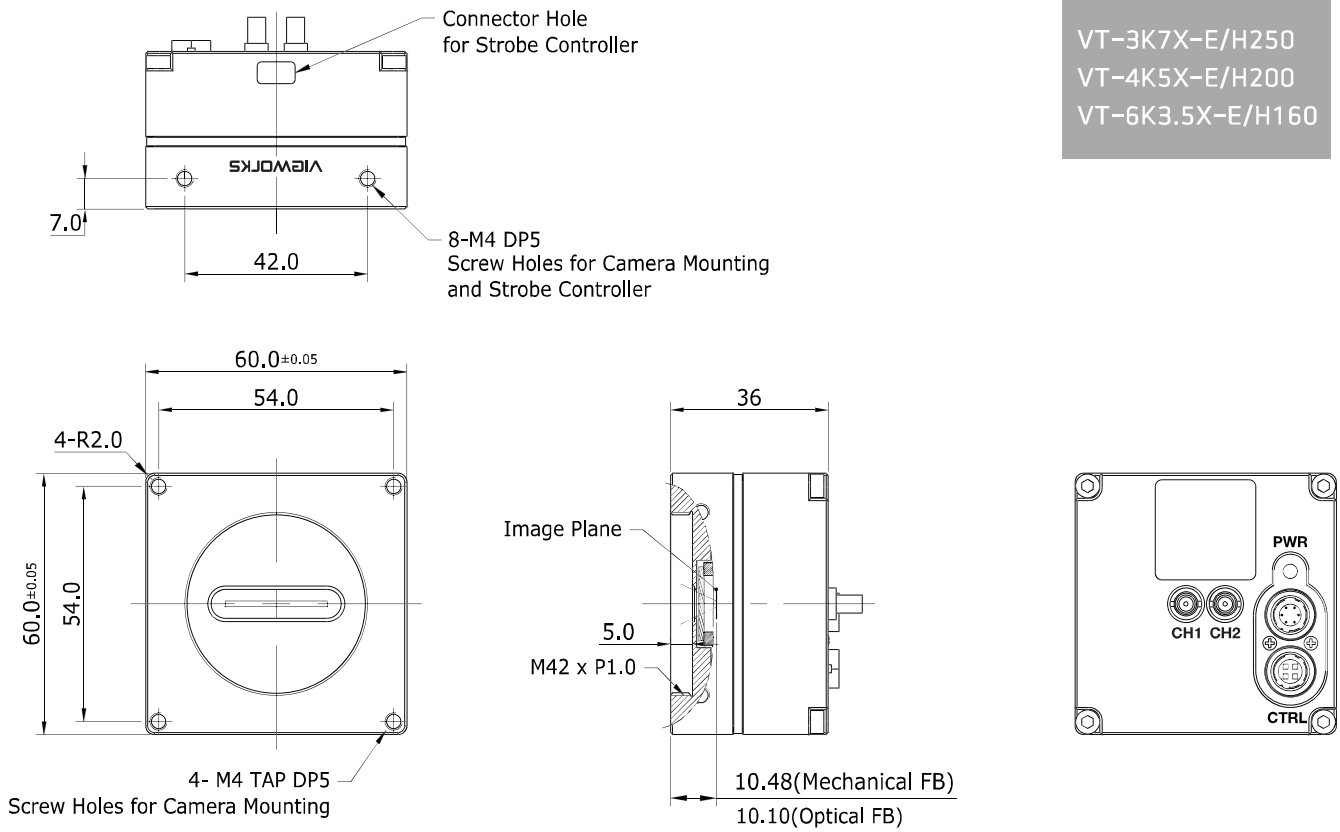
M42 mount 지원 VT CXP Series Mechanical Dimension
